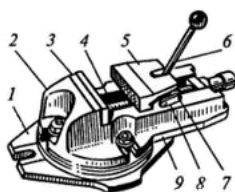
Быстродействующие машинные тиски с рычажно-кулачковым зажимом: 1 – корпус; 2 – поворотная часть; 3 – неподвижная губка; 4 – винт; 5 – губка; 6 – рукоятка; 7 – эксцентриковый вал; 8 – двойной кулачок; 9 – основание
